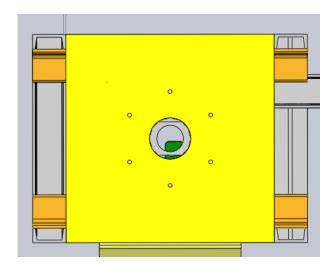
Vista frontal del porta molde, parte superior e inferior.
